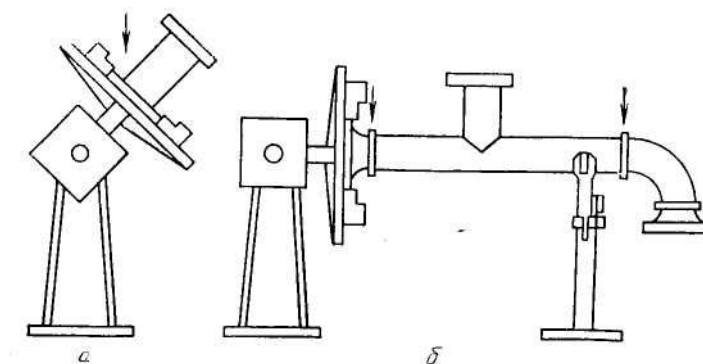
Маніпулятори: а – для приварювання фланця; б – для зварки вузла з приварюванням комірною фланця і відводу.
